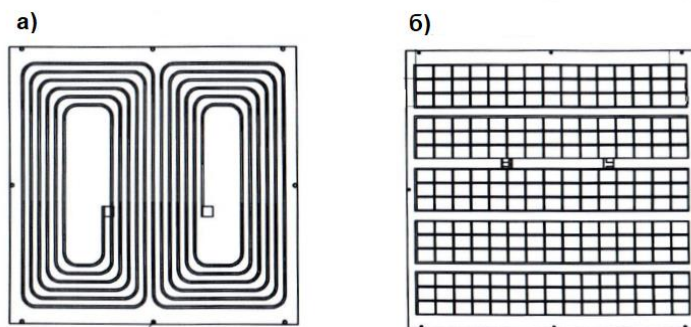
Сборочный вид передатчика оснастки и инструмента: а) вид сверху; б) вид снизу *Fig. 7. Assembly view of the repetition: a) top view; b) type of base
